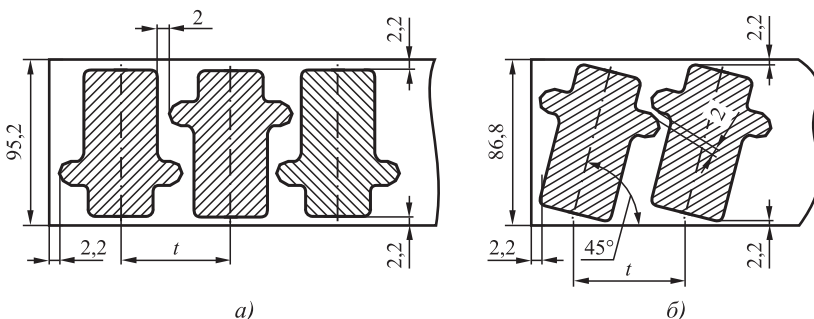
Варианты расположения заготовок в полосе: а — прямой раскрой; б — наклонный раскрой
